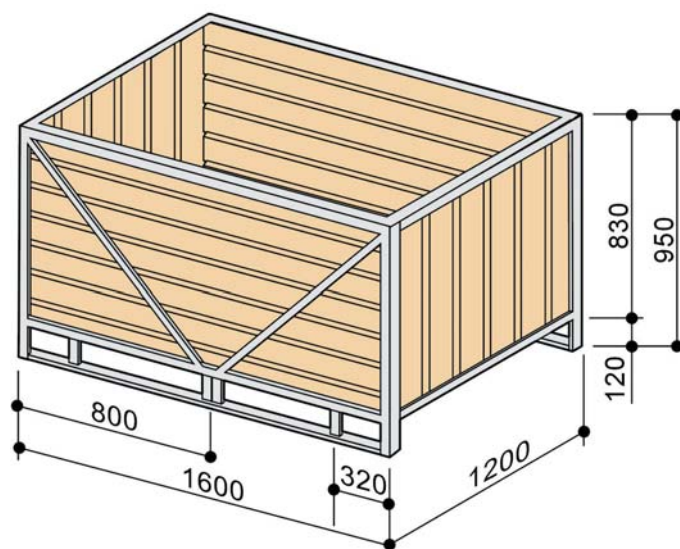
Paletový sklad brambor hůře využívá obestavěný prostor
